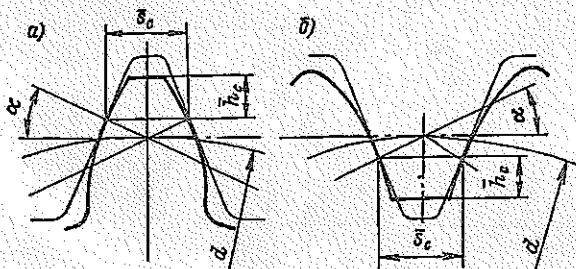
Схема замера постоянной хорды: а — для зубчатых колес с внешними зубьями; б — для колес с внутренними зубьями
